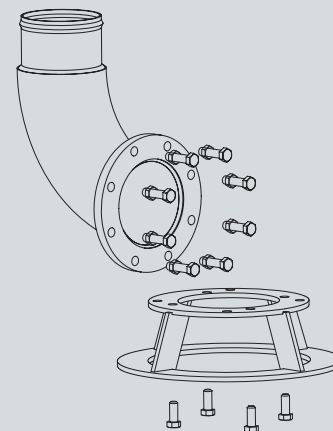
Ringständer mit 90°-Rohrbogen und Anschluss mit Außengewinde
